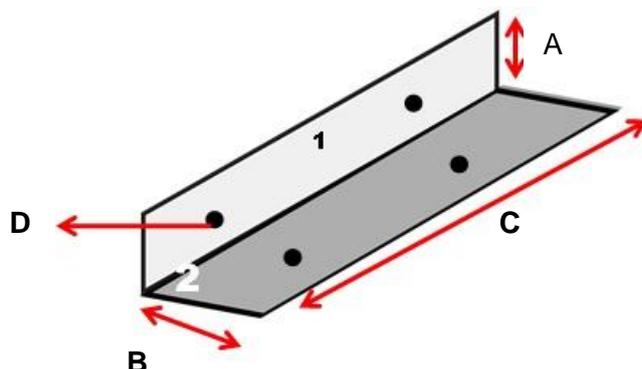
Así es como debe de quedar tu soporte del adaptador.
